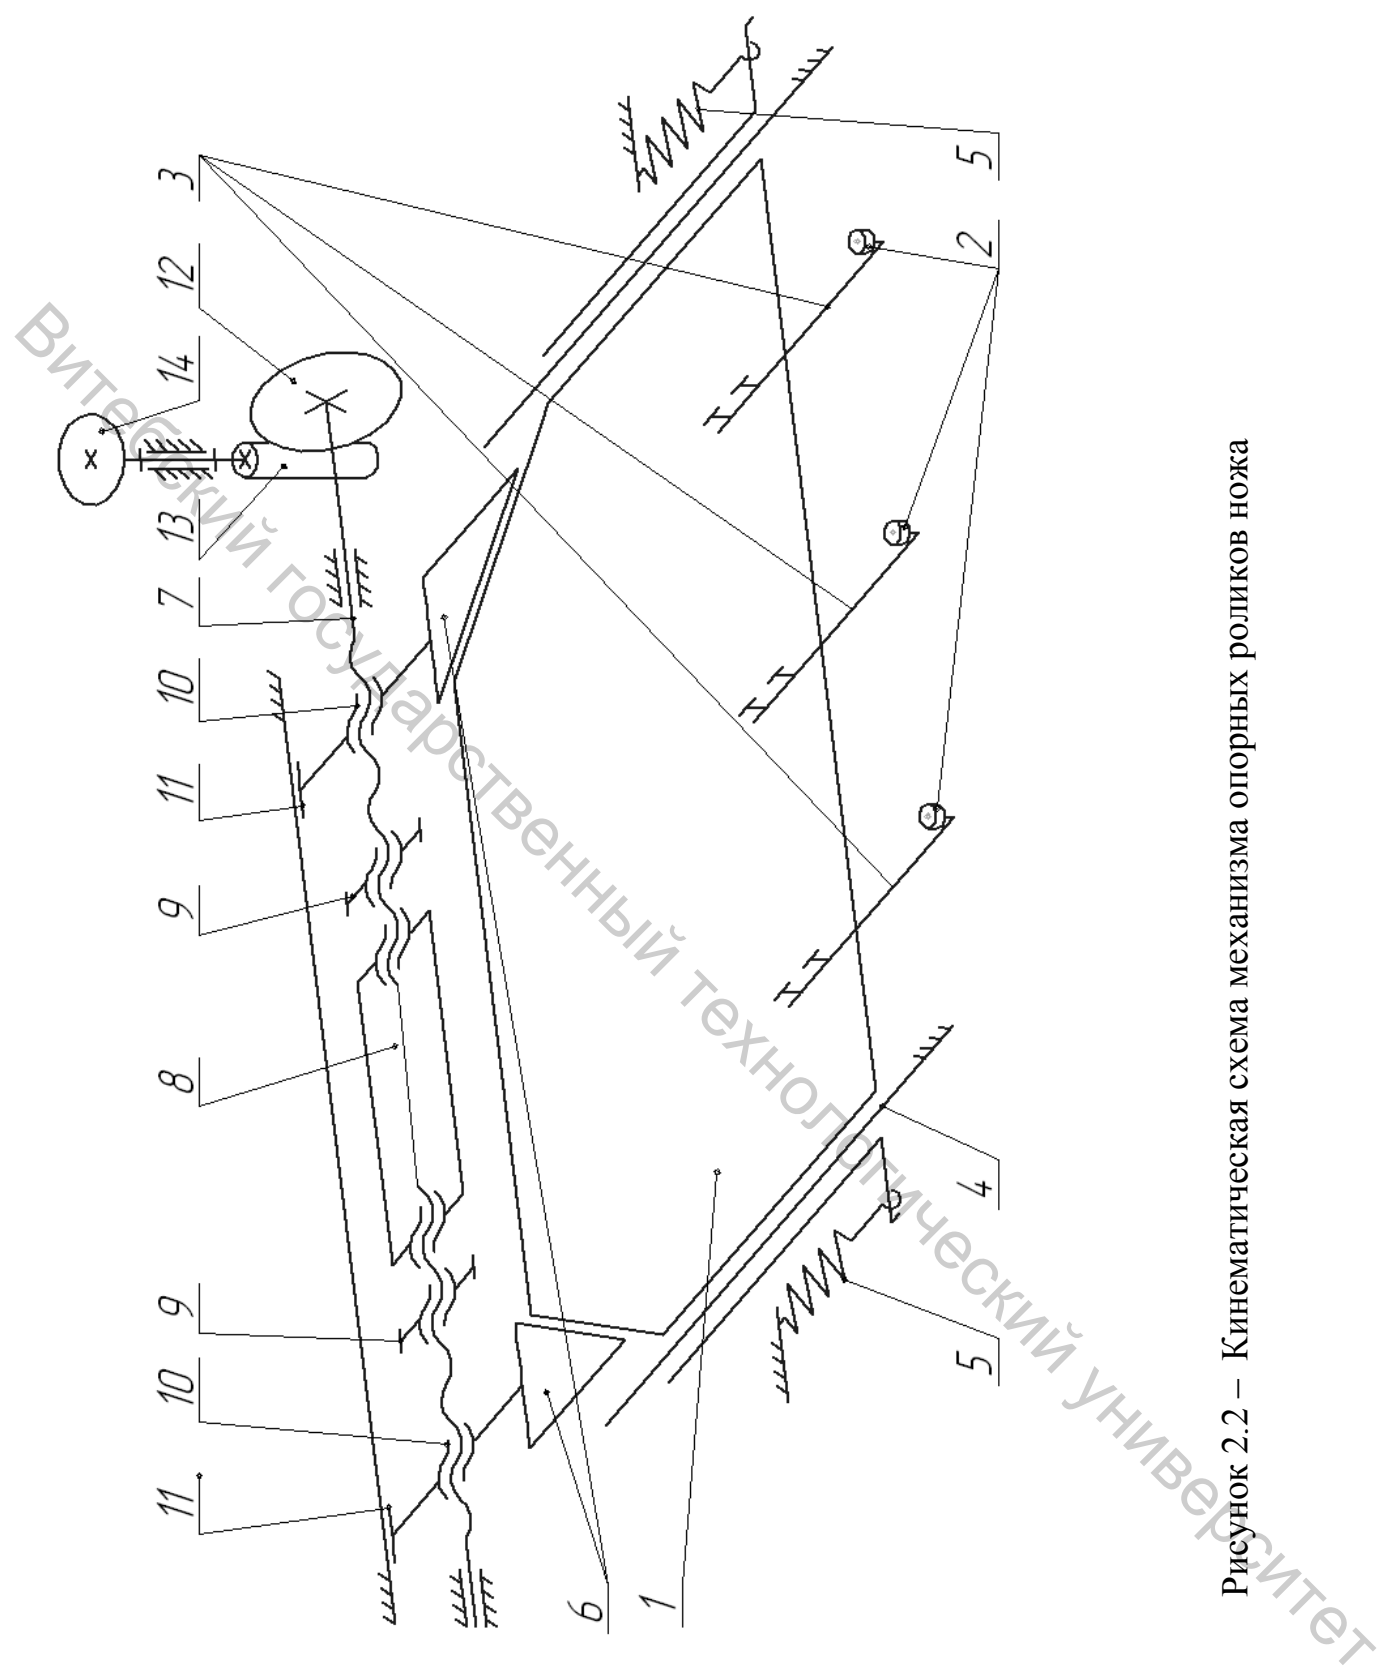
Кинематическая схема механизма опорных роликов ножа
